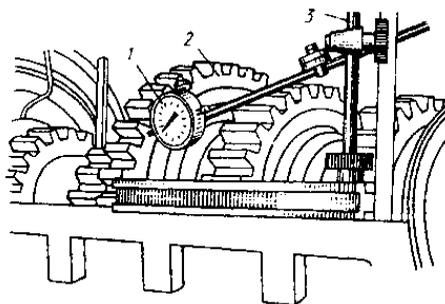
Проверка шестерни на биение торцевой поверхности:
